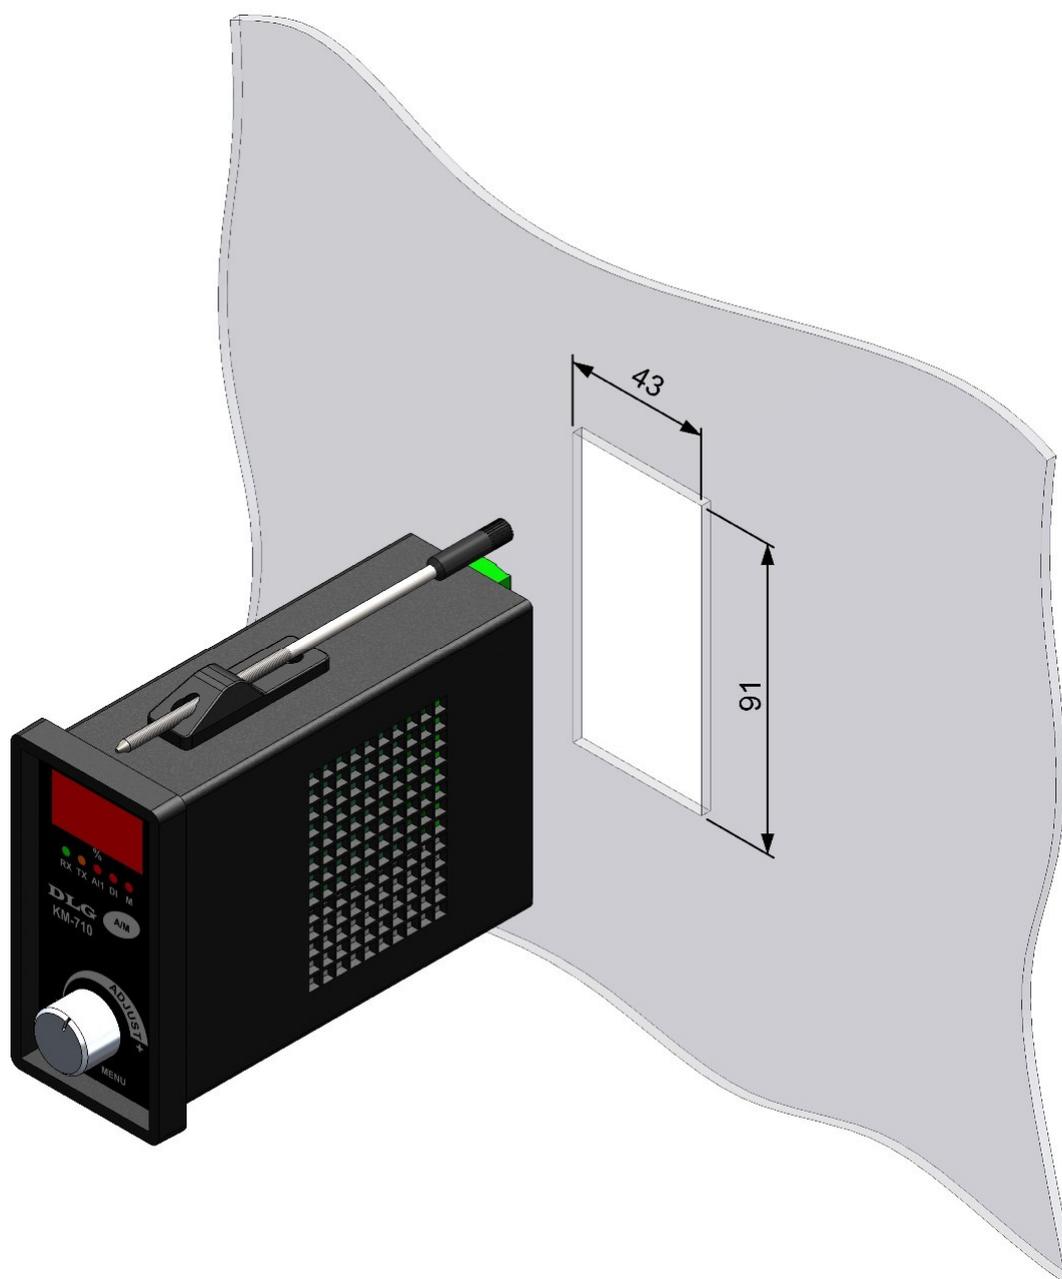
Dimensionamento para montagem da KM-710, 43 x 91 (Cotas em milímetro)
